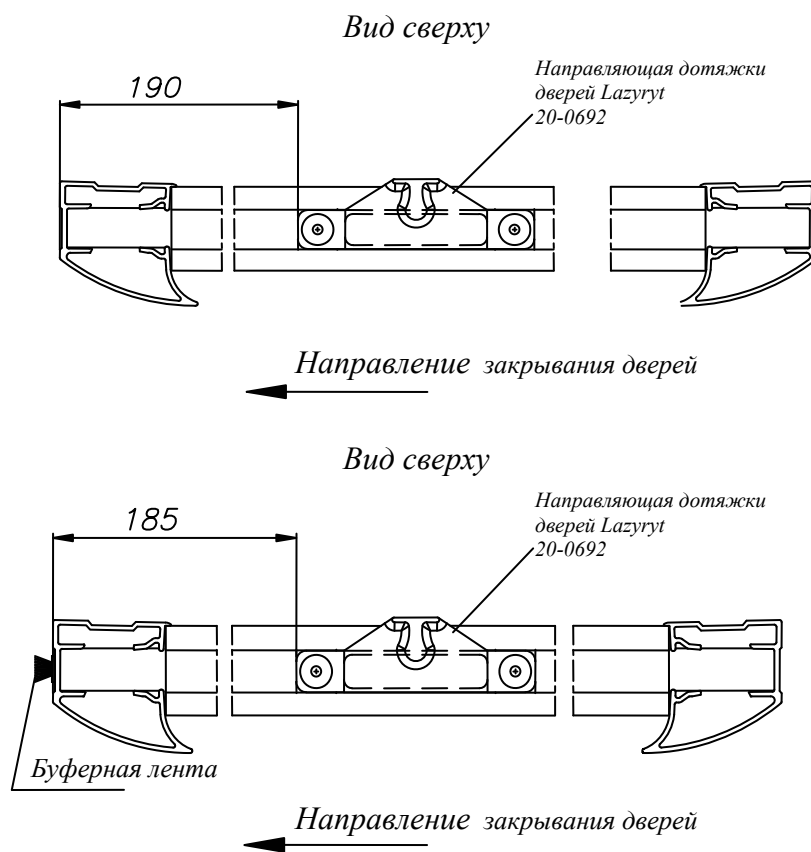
Крепление зацепки к верхнему горизонтальному профилю
